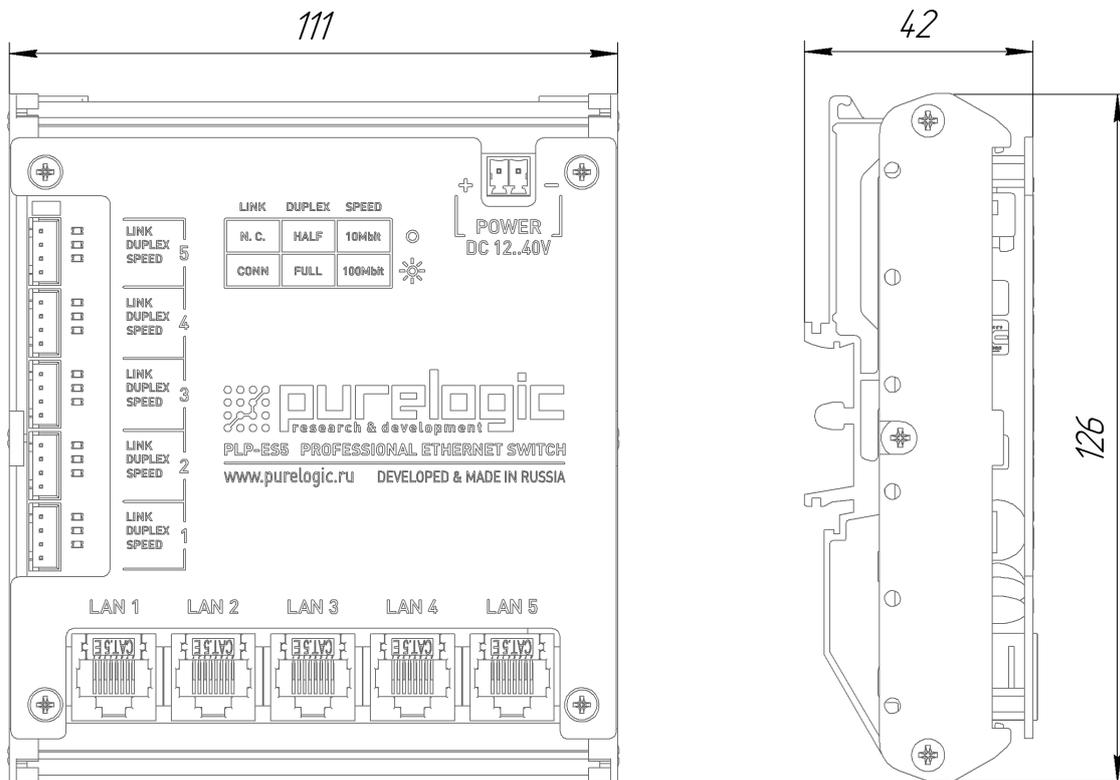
Габаритные размеры в исполнении крепления на DIN-рейку
